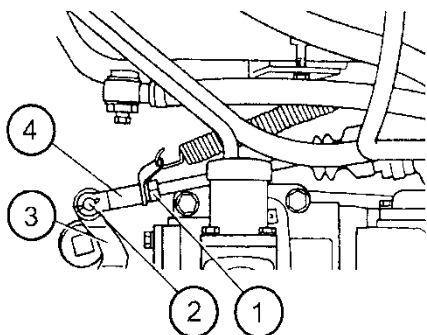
Регулировка механизма управления сцеплением: 1 – контргайка; 2 – палец; 3 – рычаг; 4 – вилка
